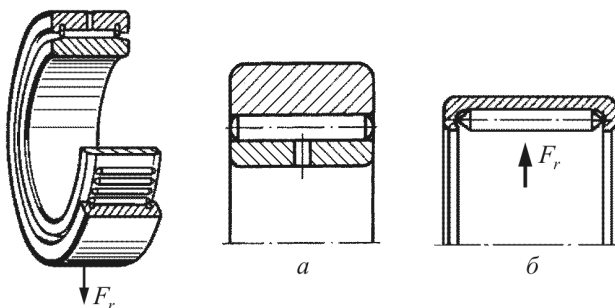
Роликовые радиальные подшипники с игольчатыми роликами
